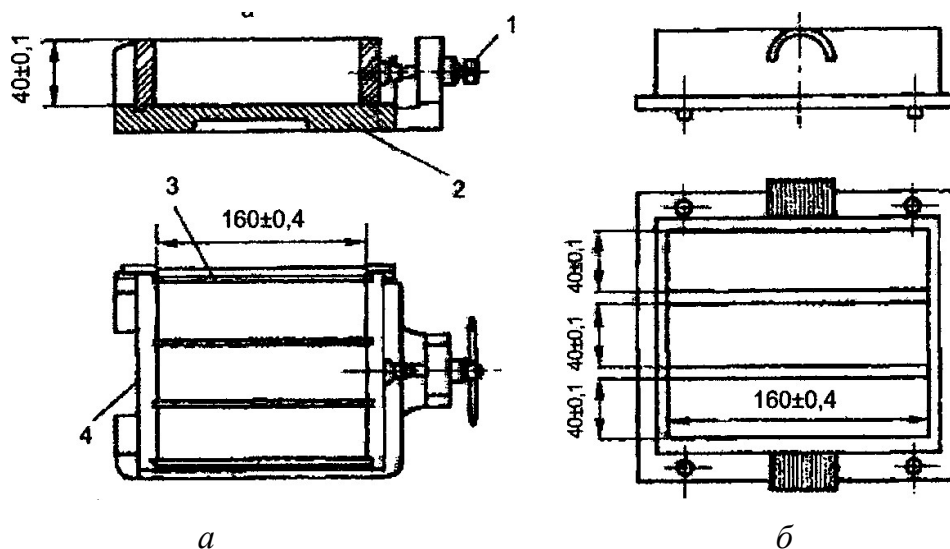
Стандартна металева форма для балочок (а) і насадка для неї (б):
